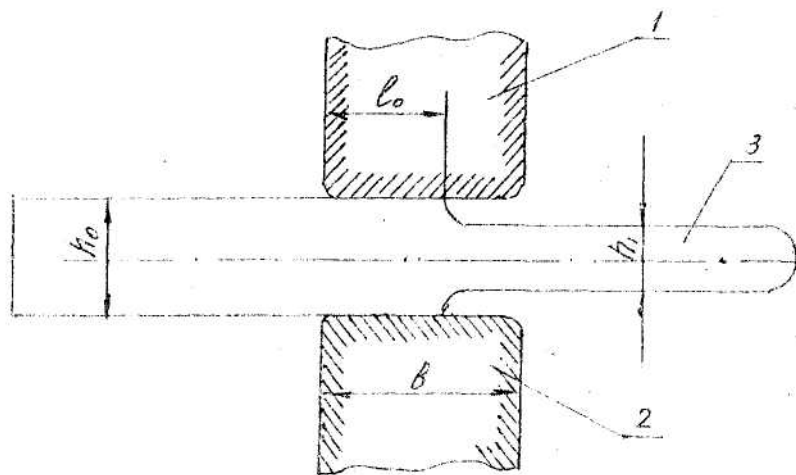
Схема протяжки: 1 - верхний боек; 2 - нижний боек;
